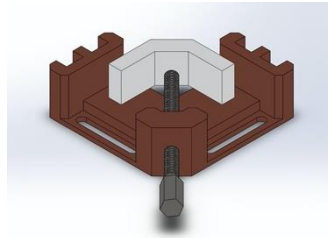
Mordaza para Soldadura en Ángulo
